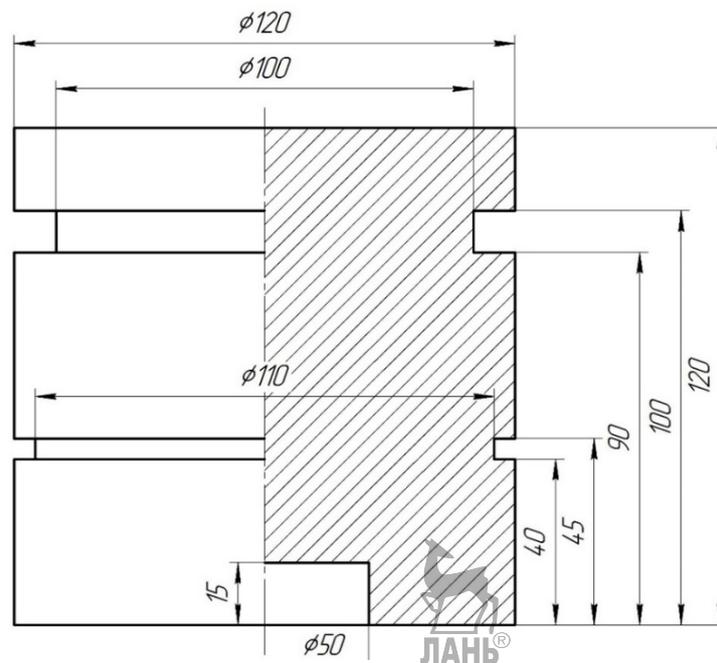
Чертеж поршня шток-рейки корпуса ОПУ
